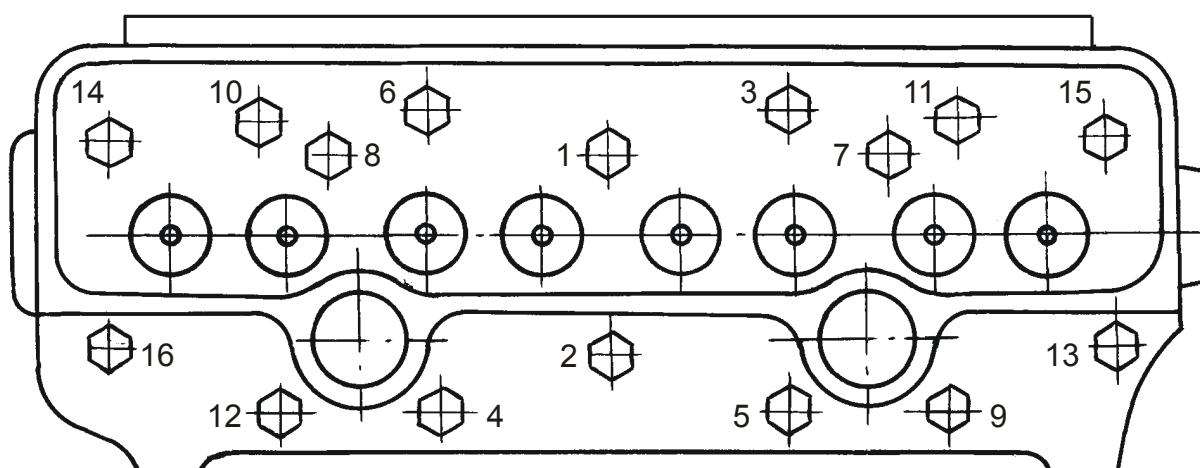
Проверка затяжки болтов крепления головки цилиндров
